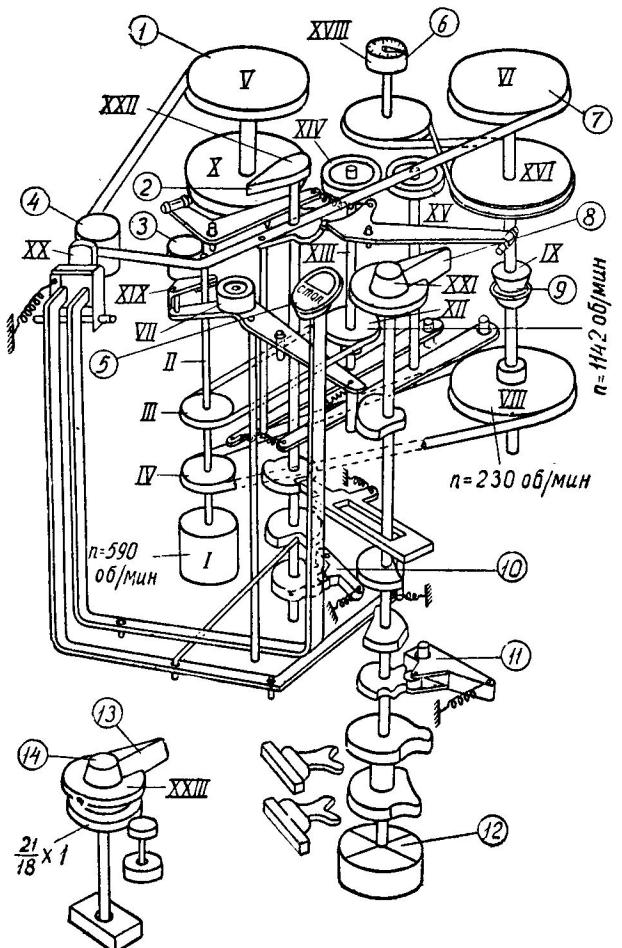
Кинематическая схема лентопротяжного механизма: 1 — подающая кассета; 2 — рукоятка управления ускоренной и обратной перемотки; 3 — универсальная головка; 4 — стирающая головка; 5 — педаль временной остановки; 6 — счетчик; 7 — принимающая кассета; 8 — рукоятка перевода рода работы; 9 — муфта проскальзывания; 10 — фиксатор на три положения; 11 — фиксатор на четыре положения; 12 — переключатель рода работы; 13 — регулятор громкости; 14 — регулятор тембра
